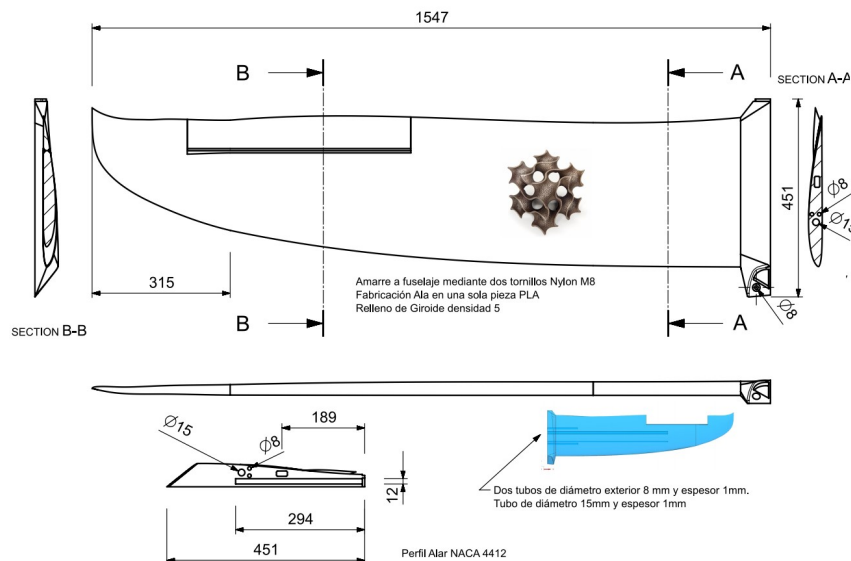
Diseño final del ala y más concretamente el perfil alar del *SolarÍO*. Para una vista más detallada de las dimensiones, se puede consultar la parte de planos del anexo 8.2.
